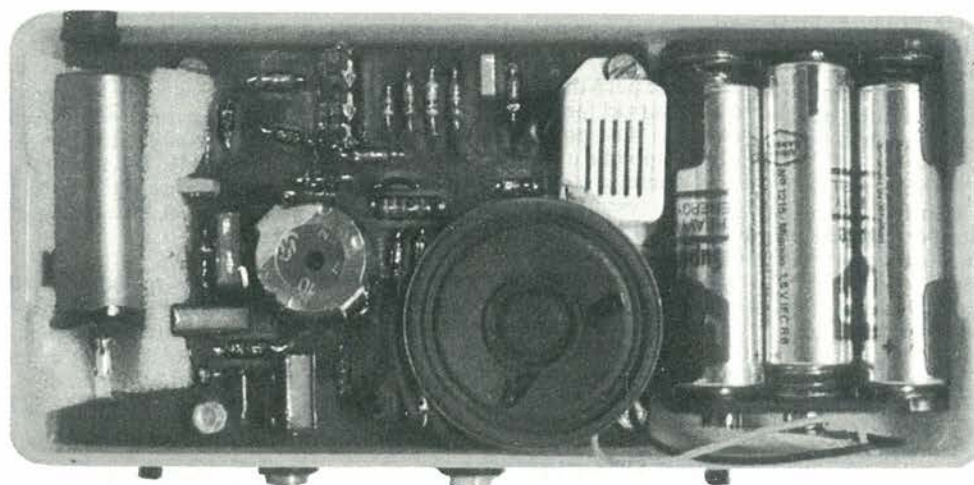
Lo strumento visto dal basso. Studiare attentamente queste foto per facilitare il corretto montaggio.
